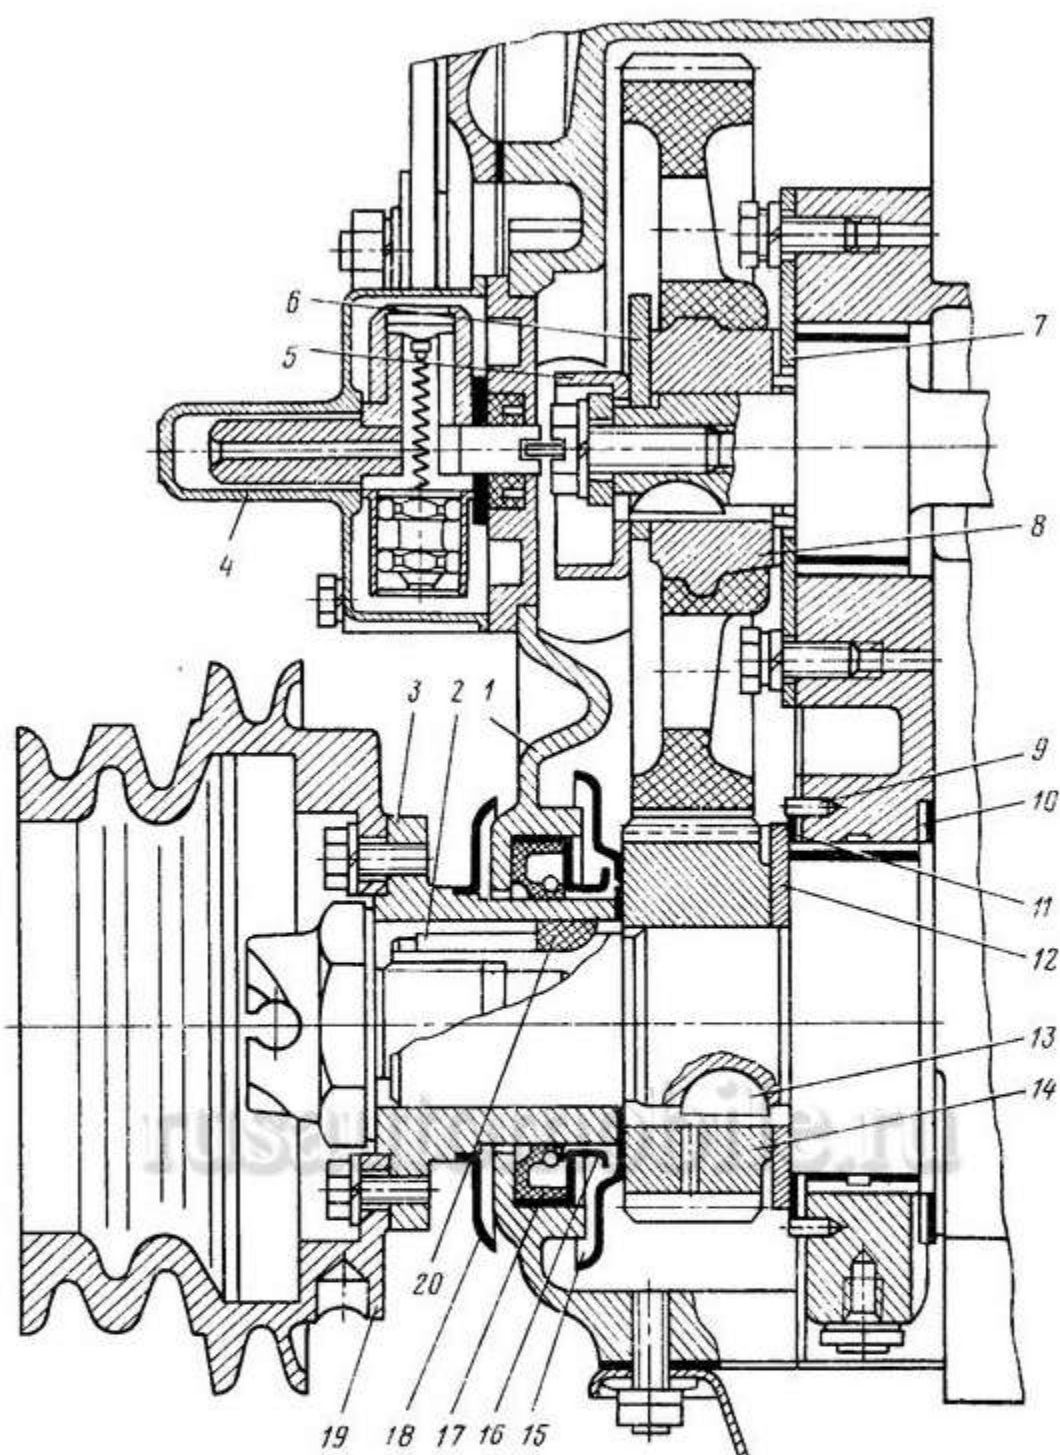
Передний конец коленчатого вала и привод распределительного вала:
